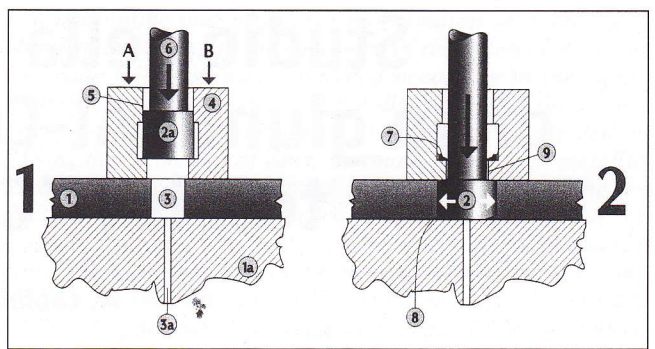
Schema di funzionamento del dispositivo per saldatura a freddo mediante tecnica cut welding utilizzato per lo studio qui presentato. 1): lastra in materiale più duttile (alluminio), 2,2a): cilindro di materiale più duro (rame), 3): foro coassiale, 4): tagliente, 5) guida, 6): sistema meccanico di compressione (punzone), 7): rame asportato, 8): alluminio pelato, 9): lama.
